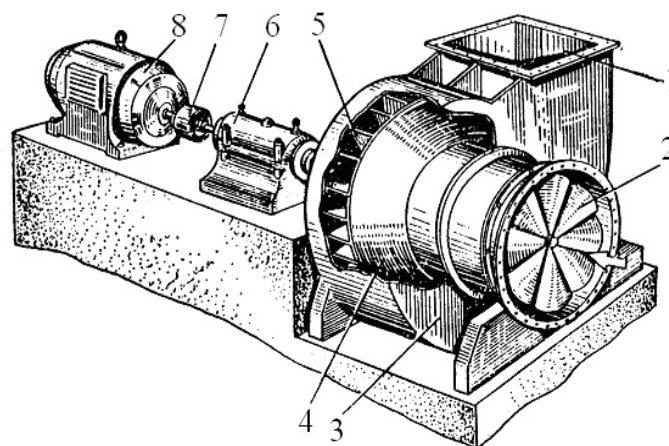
Дымосос (дутьевой вентилятор) одностороннего всасывания: 1 – выходной патрубков; 2 – поворотные лопатки направляющего аппарата; 3 – улиткообразный кожух; 4 – ротор; 5 – рабочее колесо; 6 – корпус подшипников; 7 – соединительная муфта; 8 – электродвигатель
